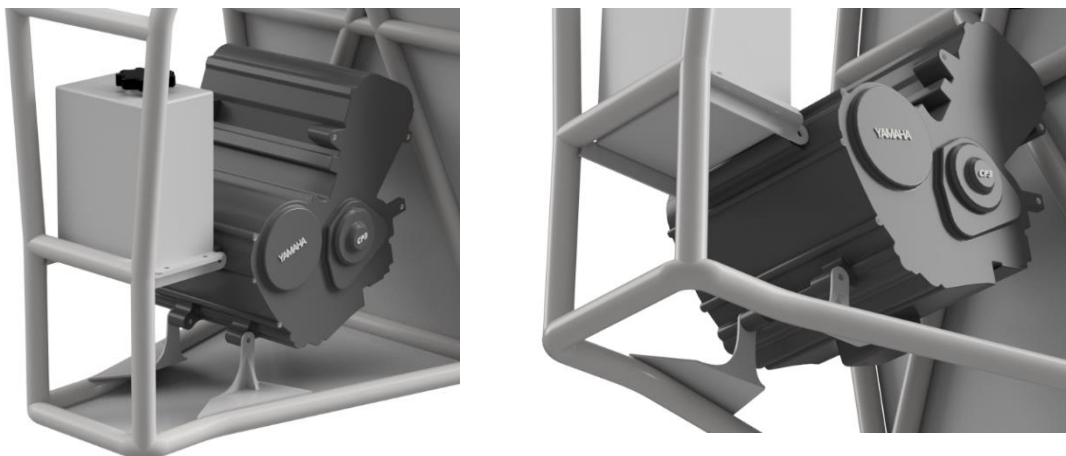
Disposición de los soportes del depósito de combustible y del motor
